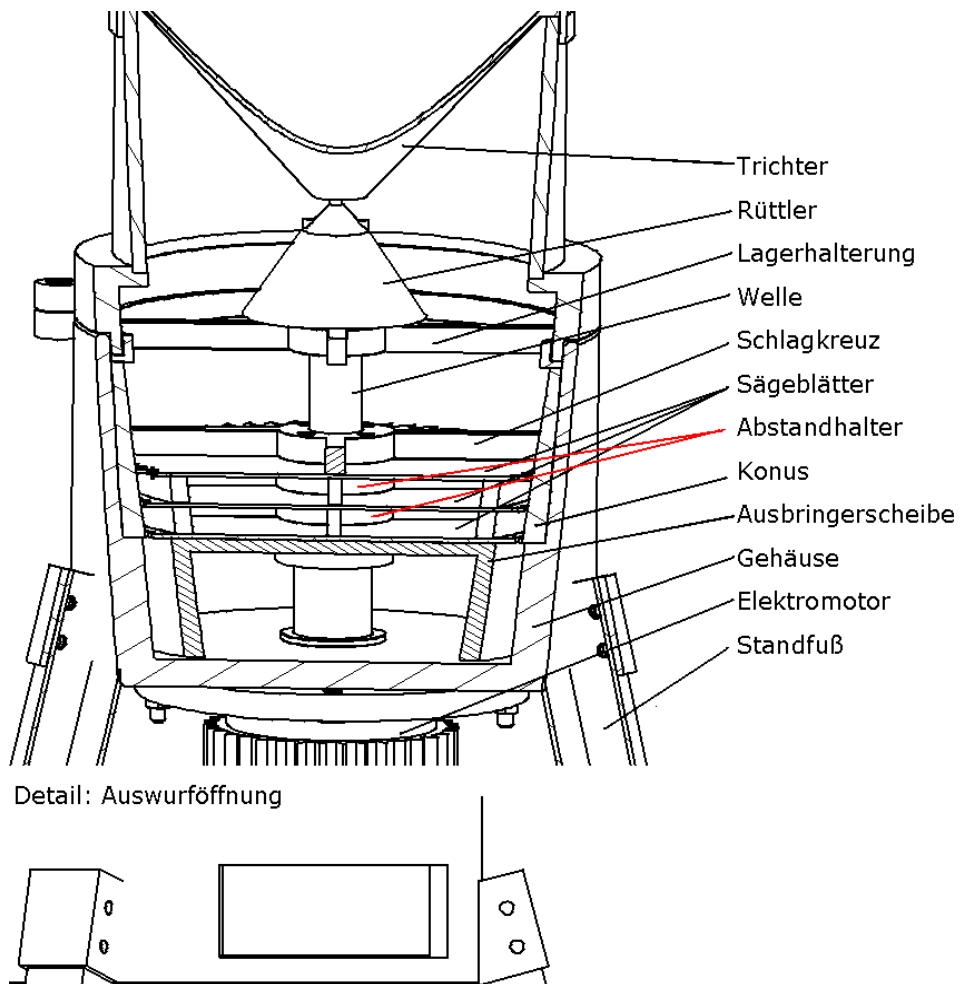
Detailansicht des Prototyp InnoMill III
